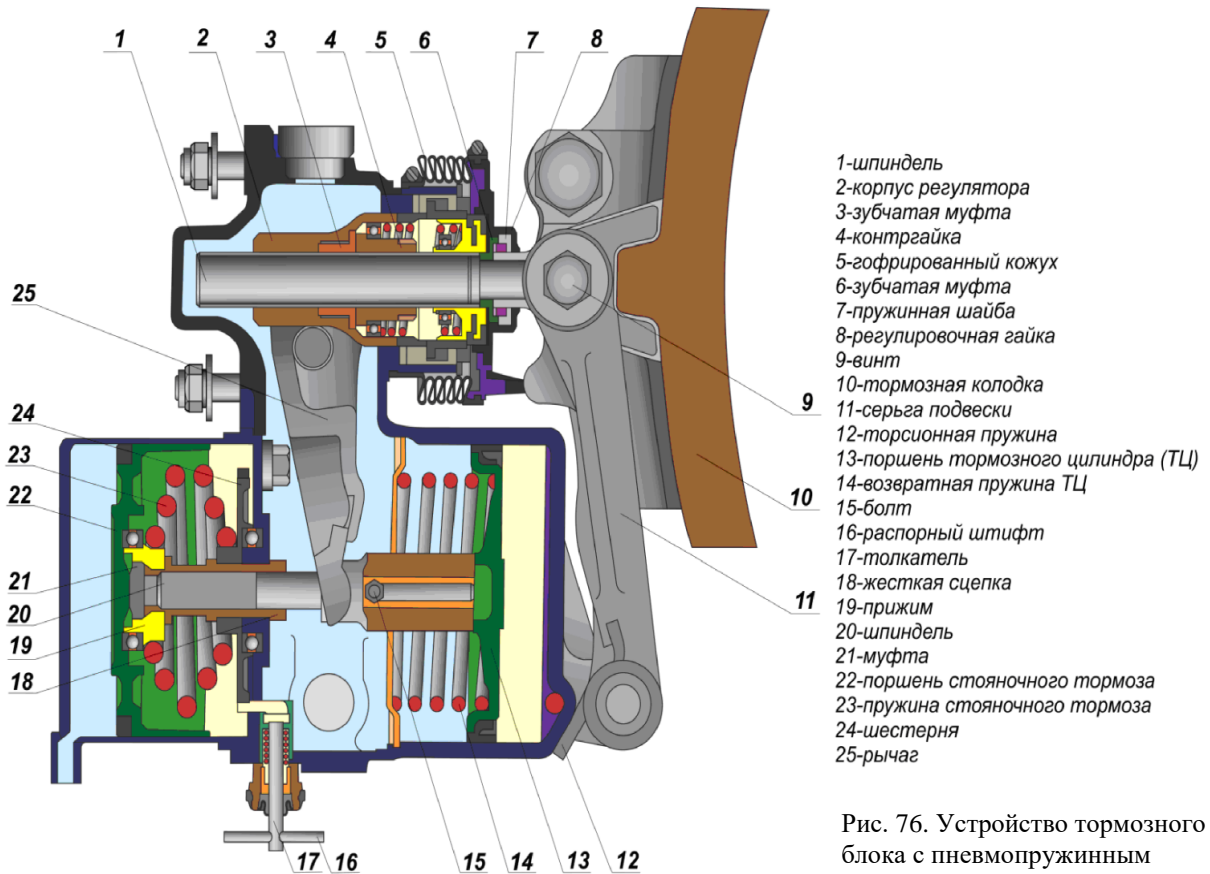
Устройство тормозного блока с пневмопружинным тормозом
